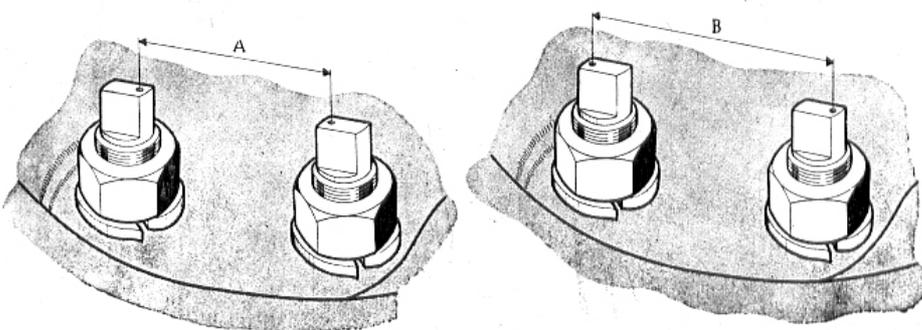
Position mini et maxi des excentriques de réglage des points fixes sur freins Bendix HC
